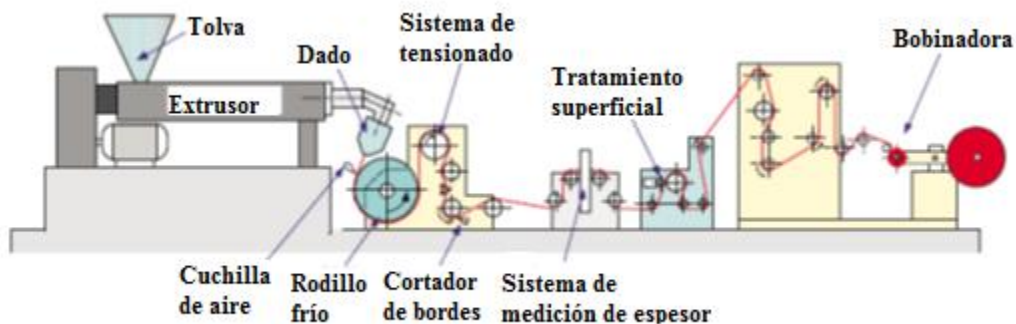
Principales componentes de una línea de extrusión por rodillos fríos.
